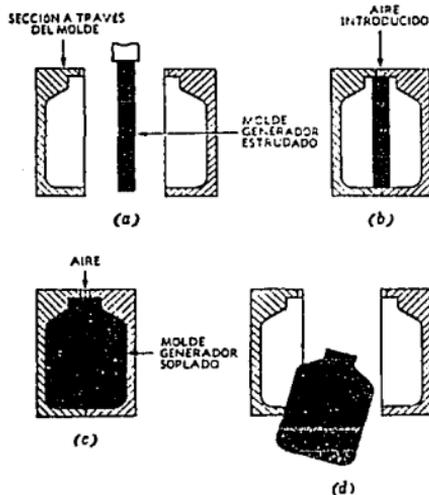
PRINCIPIOS BASICOS DEL MOLDEO POR SOPLADO (EXTRUSION)
